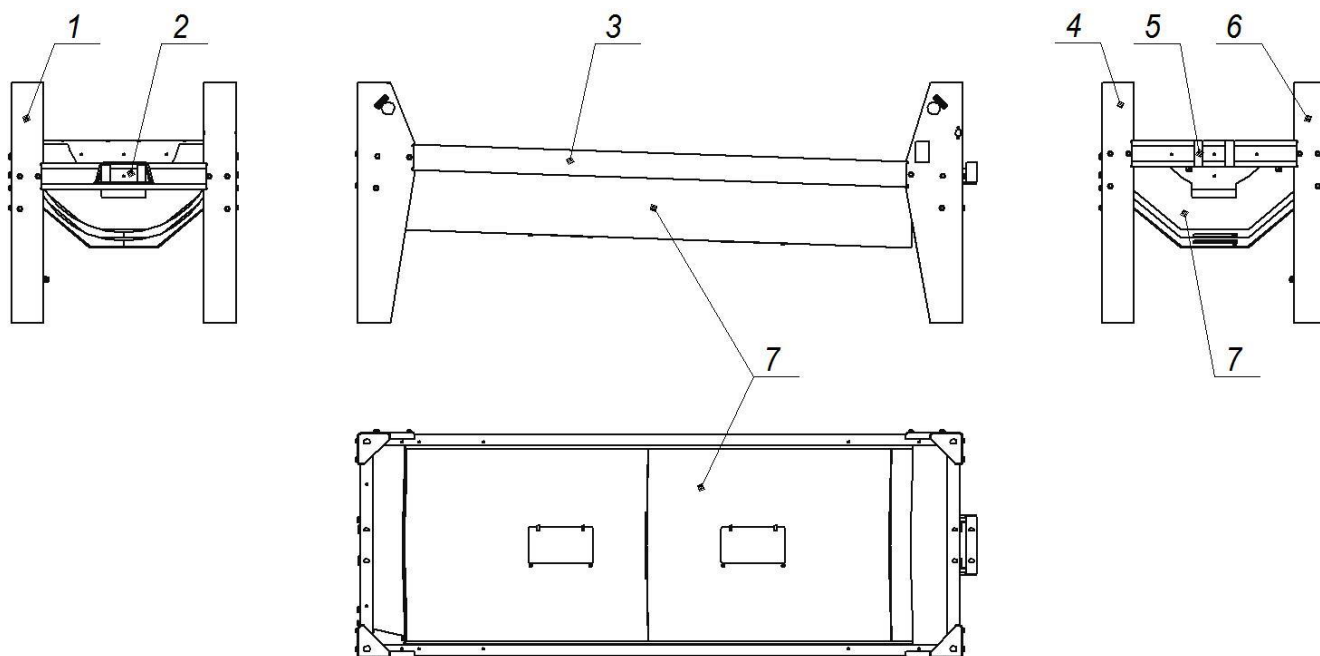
а – Рама ТК-800-8Е; ТО-800-8Е:
